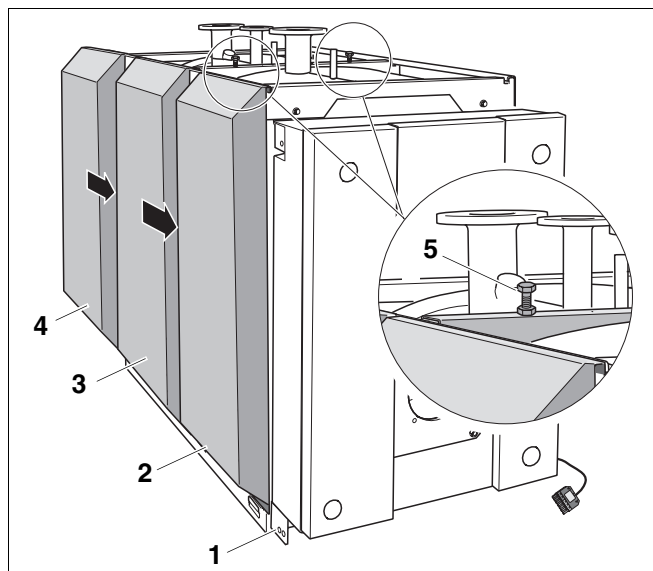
Montage des panneaux latéraux gauches arrière et central
